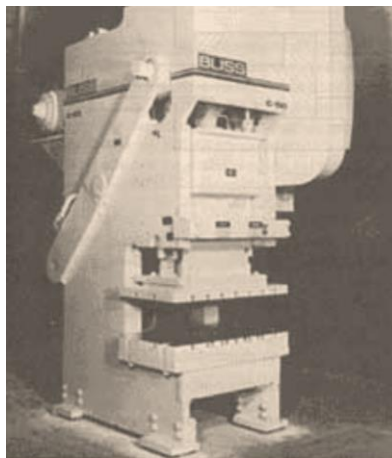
5 Componentes de una prensa con transmisión mecánica. Fuente [36]
